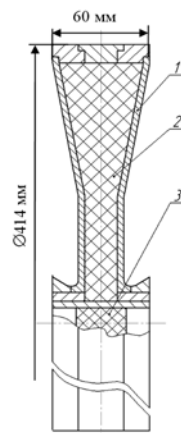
Конструкция профилированного диска $\varnothing 400$ мм: 1 – тарель (пластина); 2 – ВВ; 3 – иницирующая часть
